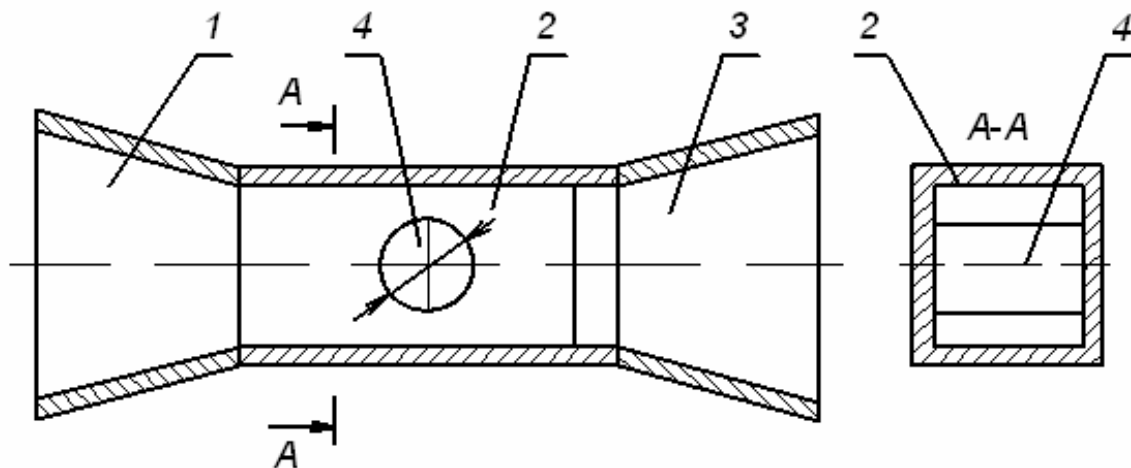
Принципова схема статичного ПКЗ: 1 – конфузор; 2 – проточна камера; 3 – дифузор; 4 – кавітатор
